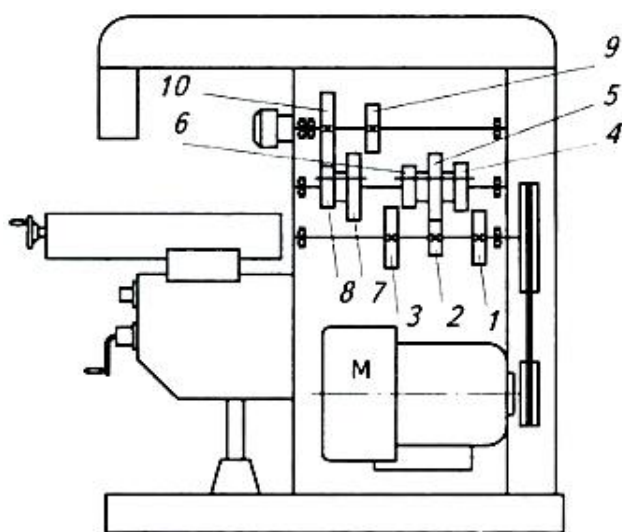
Упрощенная кинематическая схема фрезерного станка НГФ-110Ш: М — электродвигатель; 1—10 — зубчатые колеса и шестерни
